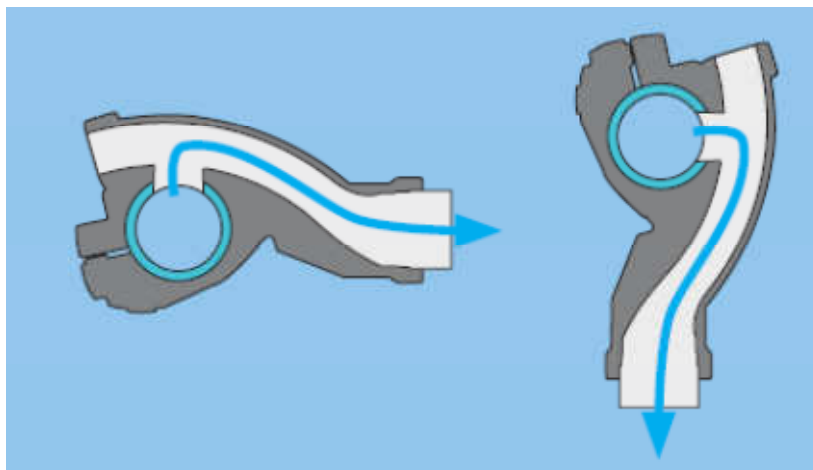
Derivação horizontal ou vertical (Fonte: Parker)
